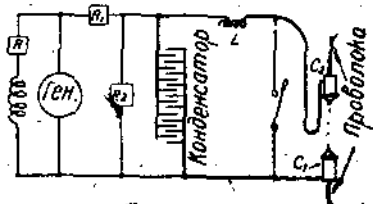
Сварочный аппарат конденсаторного типа.
